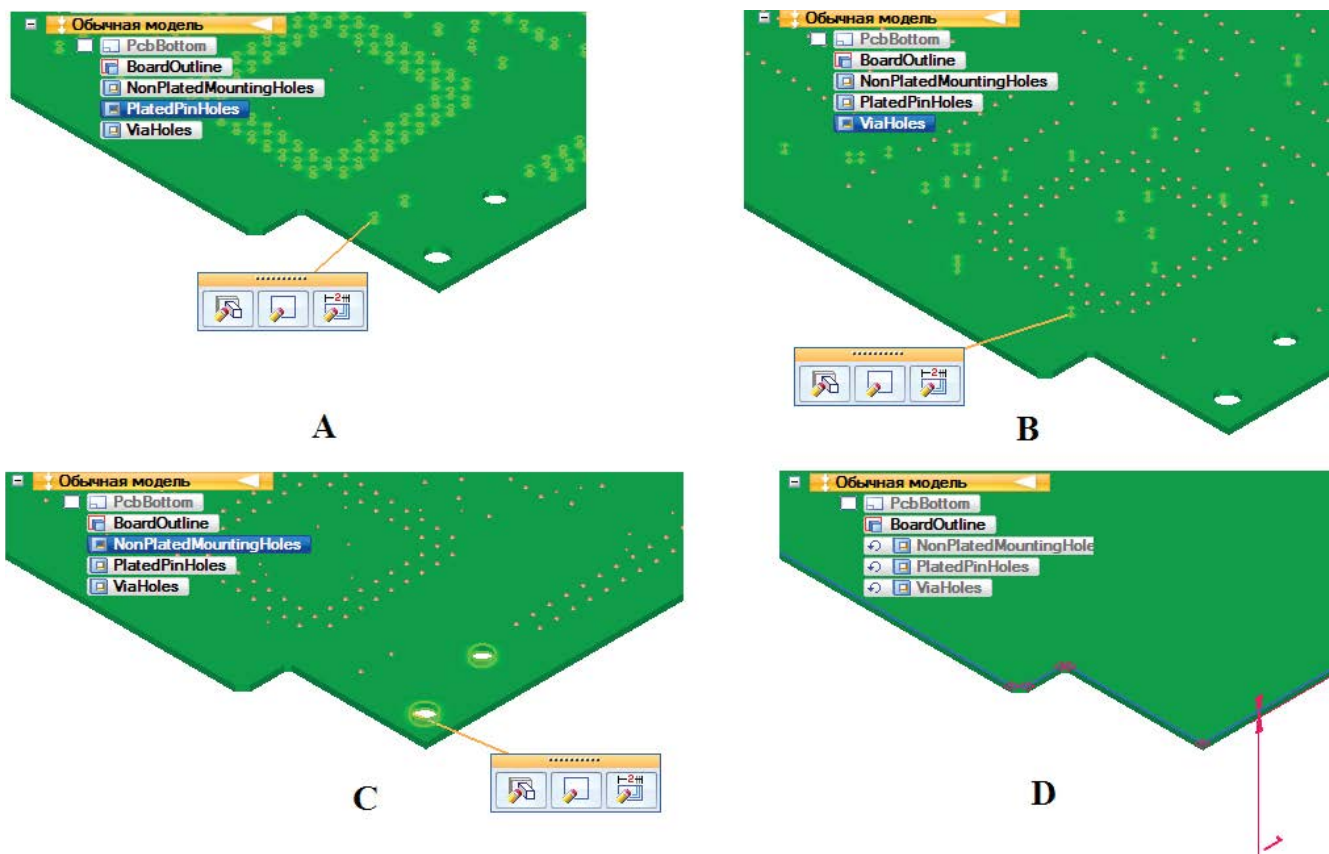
Импортированная деталь Печатная плата (укрупненный вид отверстий различного типа и контура платы)
